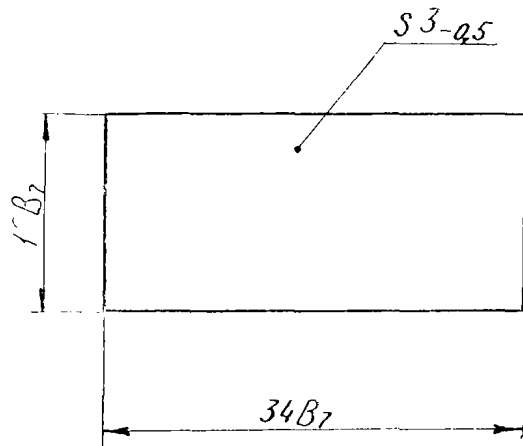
Прокладка прямоугольная, пенополиуретан
